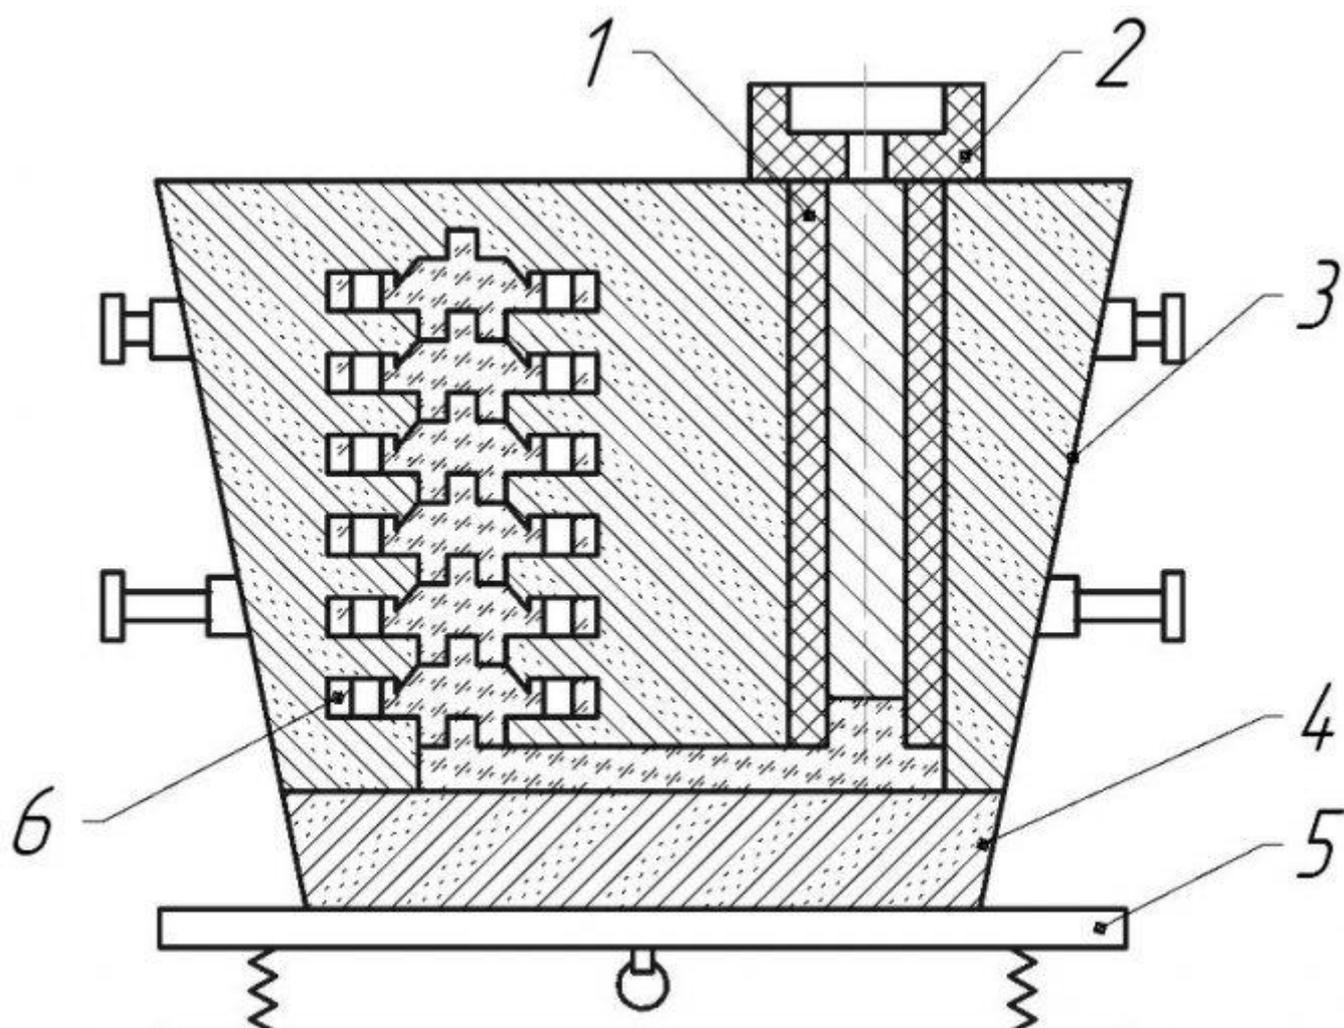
Изготовление формы с пенополистироловой моделью без связующего: 1 – керамический стояк; 2 – чаша; 3 – опока-контейнер; 4 – предварительная засыпка; 5 – вибратор; 6 – блок моделей
